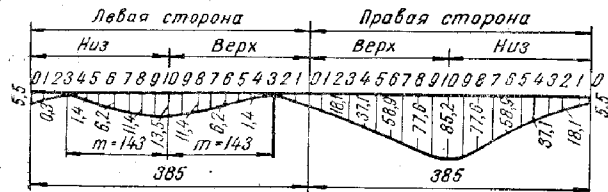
Развертка конца отростка сварного тройника.
